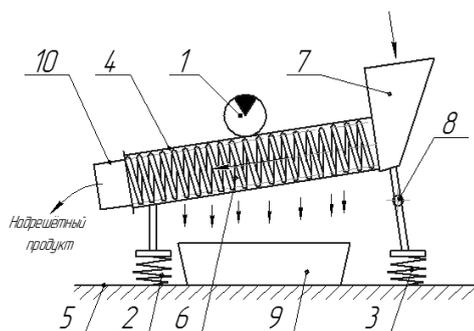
Схема экспериментальной установки пружинного грохота: 1 – вибропривод; 2, 3 – амортизаторы; 4 – корпус; 5 – рама; 6 – просеивающая поверхность; 7 – загрузочный патрубкок; 8 – устройство для регулировки угла наклона; 9 – сборник материала; 10 – механизм регулирования границы разделения
